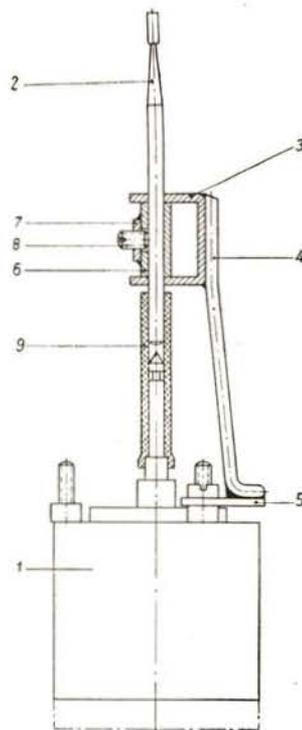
Lagerung des Bohrers am Man:perm-Motor (Maßstab 1 : 1)
